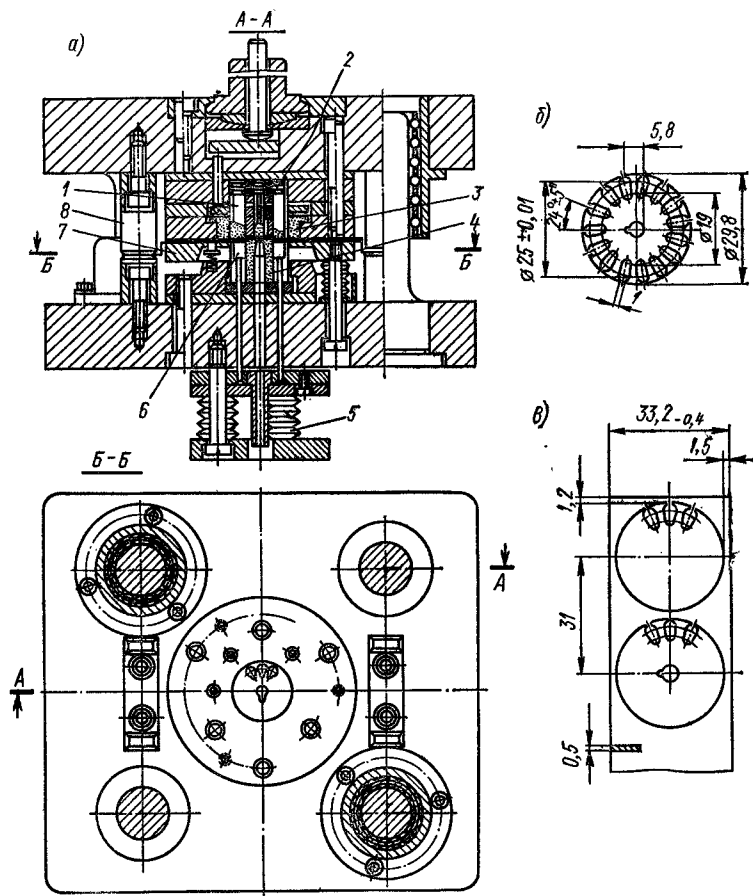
Вырубной совмещенный штамп с твердосплавными рабочими частями: а — конструкция штампа; б — штампуемая деталь; в — раскрой полосы
